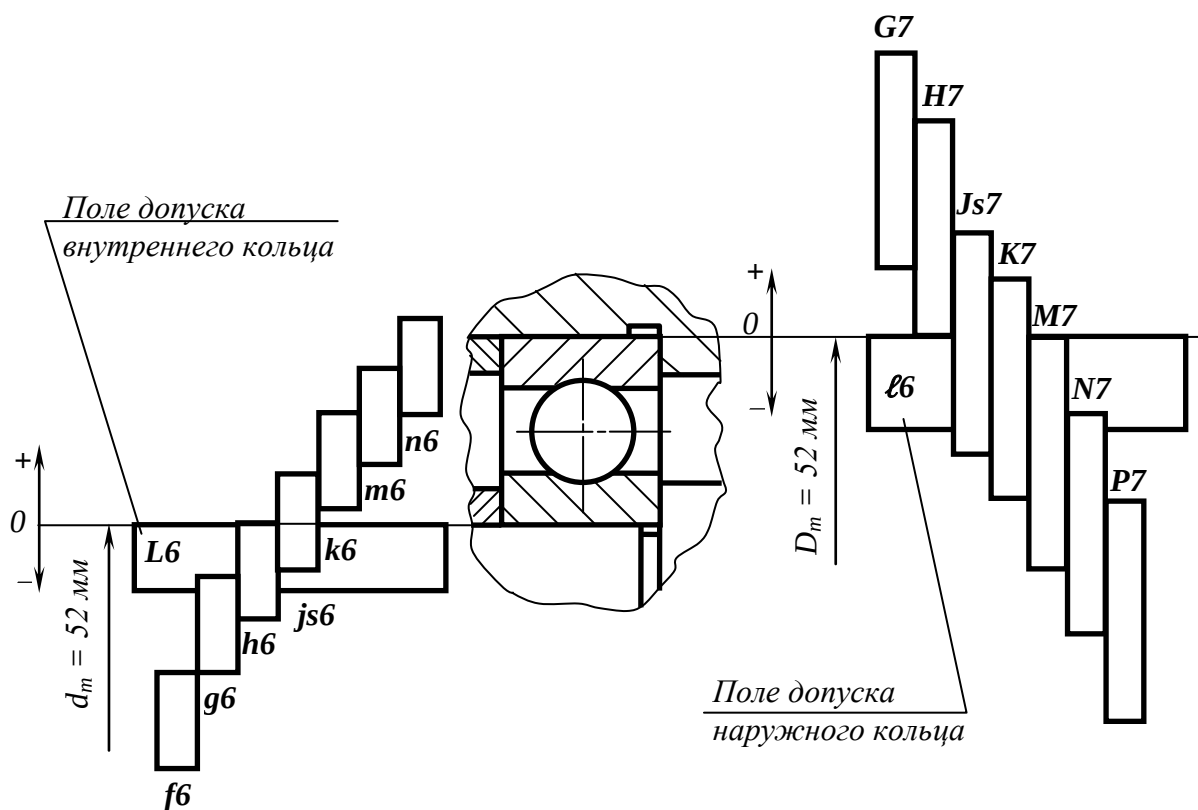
Схемы полей допусков посадок подшипника 6-205 в корпус и на вал
